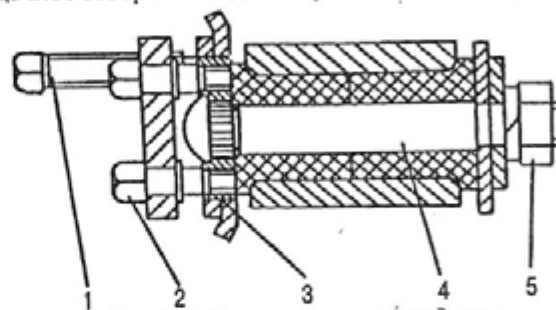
Съемник пальца переднего кронштейна задней рессоры: 1 и 2 - винты; 3 - шайба; 4 - палец; 5 - гайка
